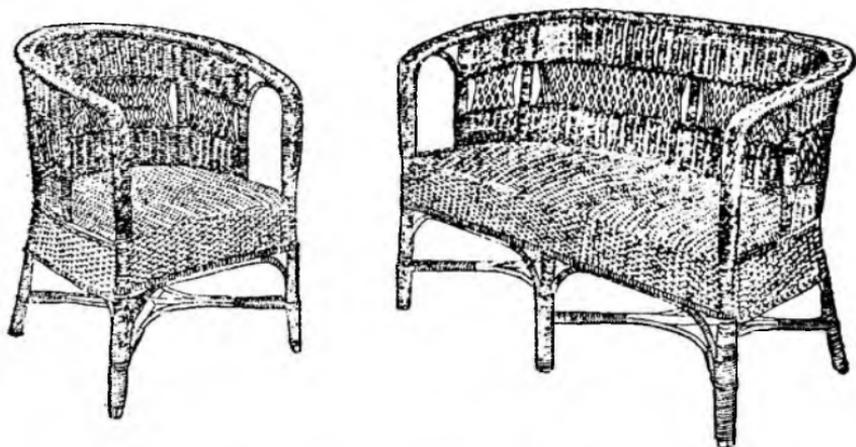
Кресло и диван в виде подковы с плетением из рогозовых лент
